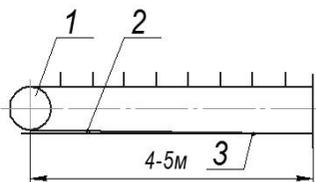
Проверка натяжения цепи транспортера ТВК-80А:
